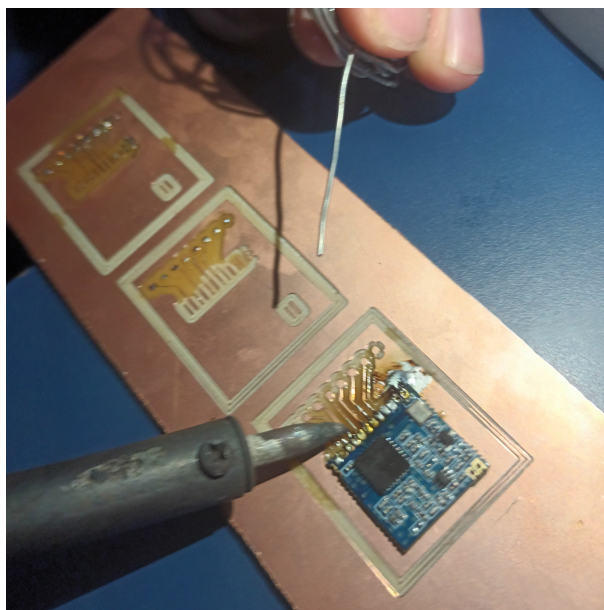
Proceso de soldado de módulo LoRa.
